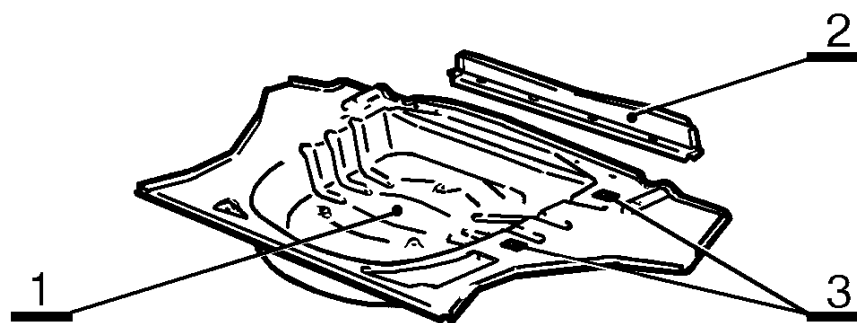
Детали пола заднего в сборе ВАЗ-2108; 2109; 2114. Номера и наименования деталей, количество сварочных точек приведены в таблице 3.
